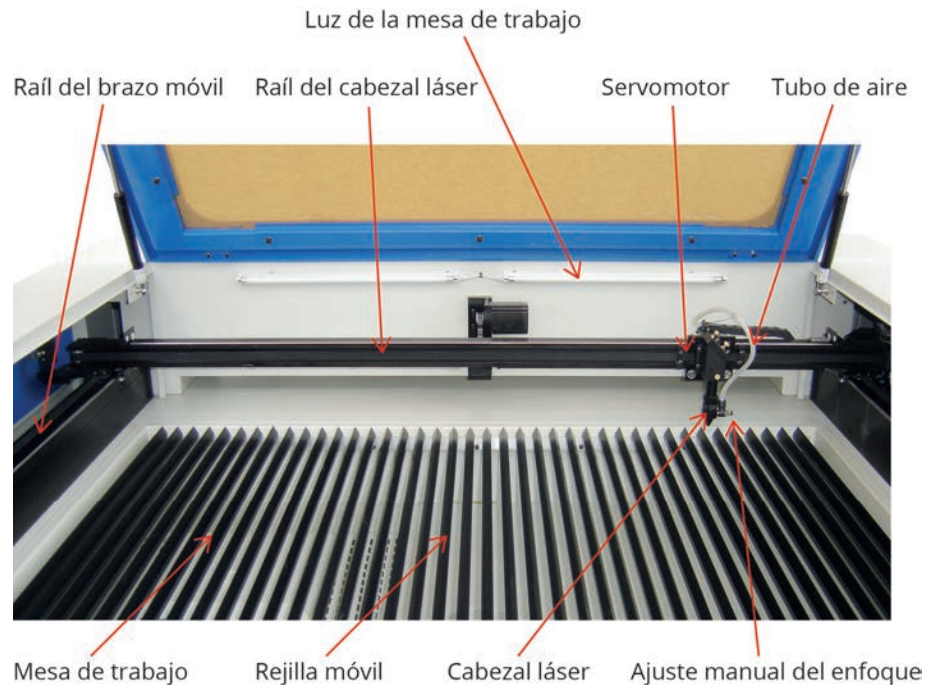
Partes básicas de una máquina de grabado láser. Recuperado en <http://www.yuehualaser.com/GS-1260-CO2-Laser-Cutter-pd6259609.html>
